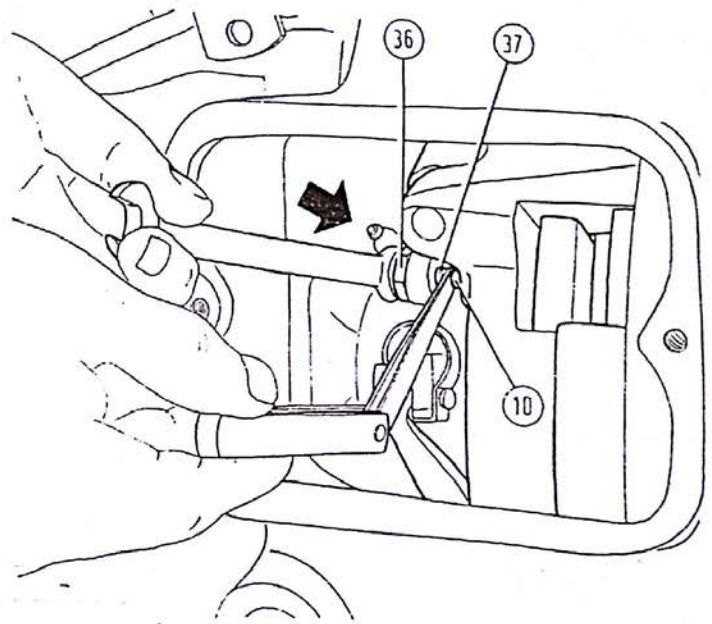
/17 - Réglage du jeu des poussoirs d'embrayage
